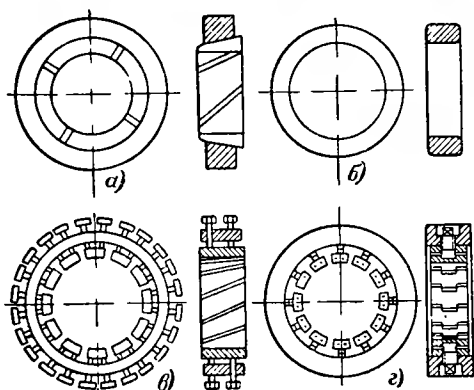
Кольца для прессовки комплекта пластин коллектора.
